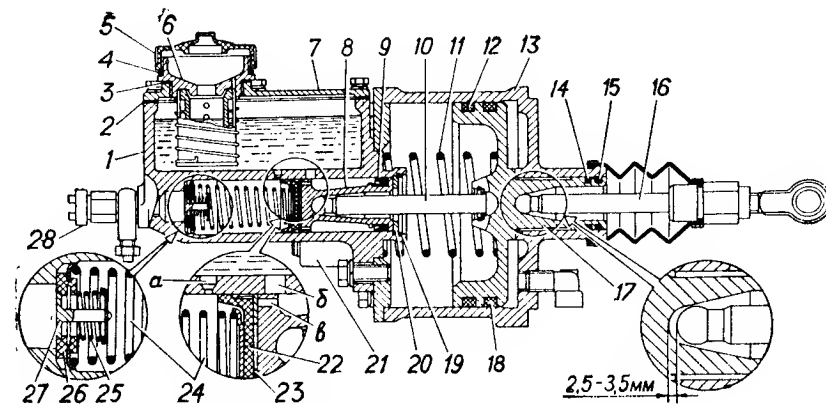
Главный цилиндр с пневмоусилителем:
